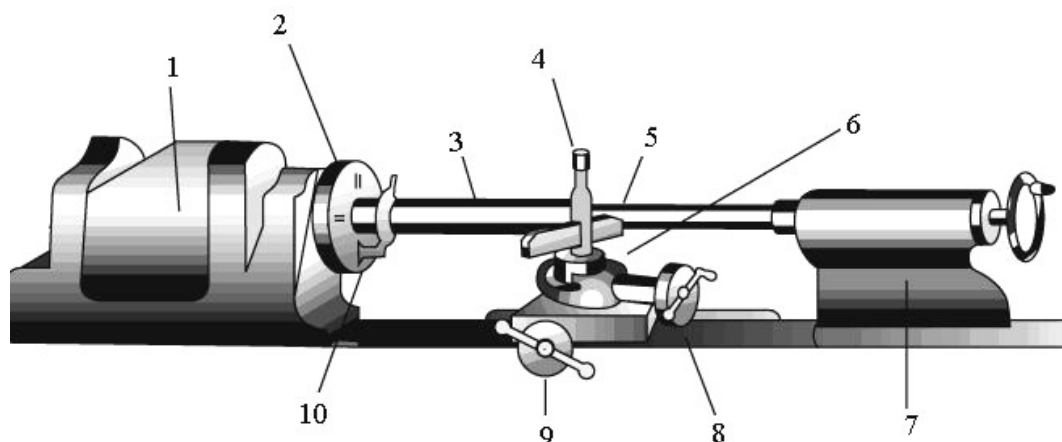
Схема универсального токарно-винторезного станка: 1 – передняя бабка; 2 – планшайба; 3 – деталь (вал); 4 – резцедержатель; 5 – резец; 6 – суппорт; 7 – задняя бабка; 8 – делительная головка; 9 – поперечная подача; 10 – токарный хомутик
